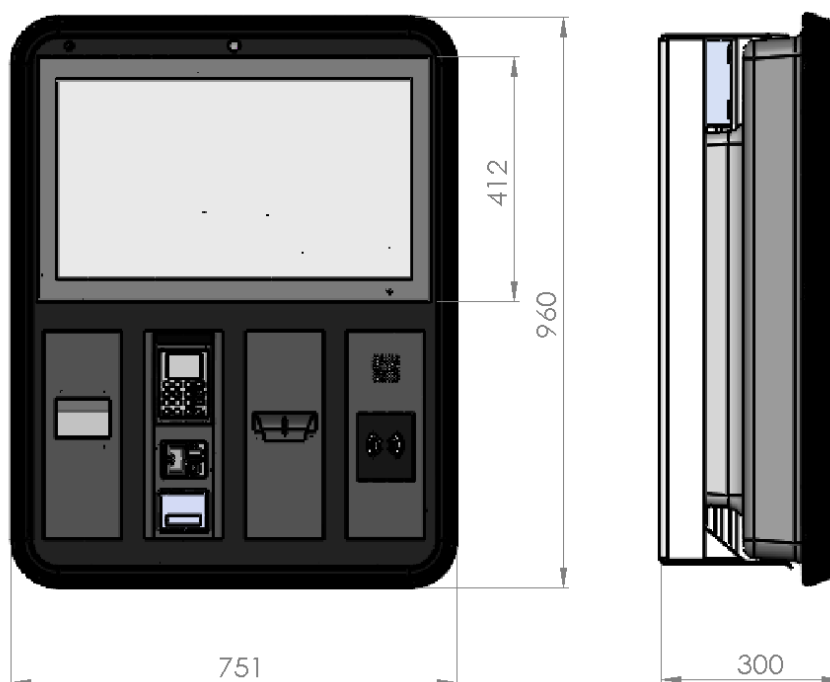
PAY FRAME 600, avec cadre lumineux, Dimensions en mm
